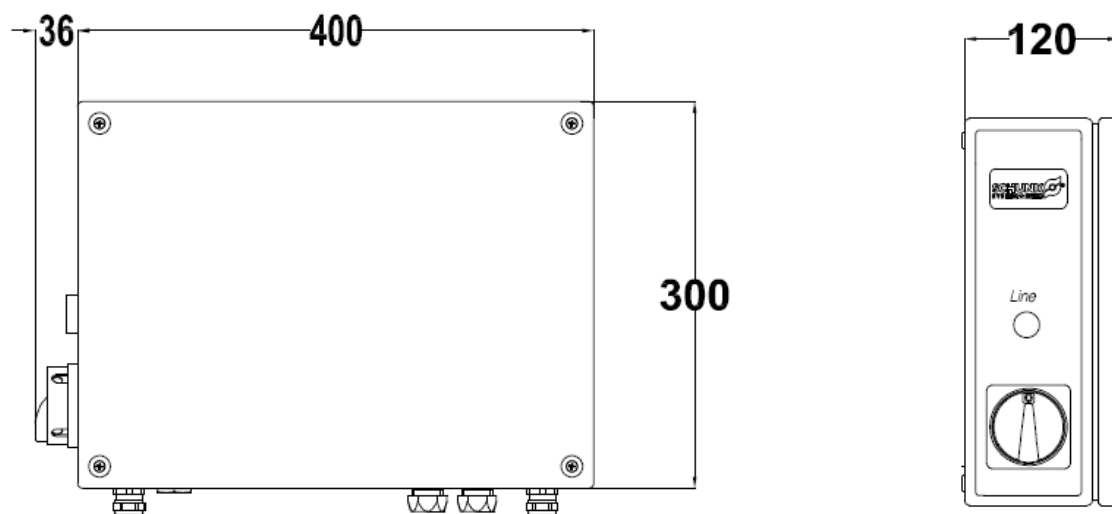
Abmessungen REBOX.1Q-SC, REBOX.2D-SC, REBOX.4-SC, REBOX.4D-SC und REBOX.8-SC
